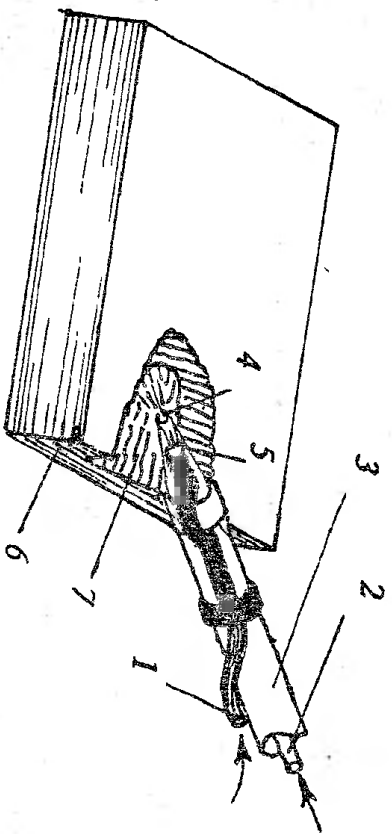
Резак для воздушно-дуговой резки. 1 — трубка подачи воздуха; 2 — подача электродной проволоки; 3 — корпус резака; 4 — дуга; 5 — солено подача сжатого воздуха в зону торения; 6 — заготовка; 7 — выплавленный участок заготовки
